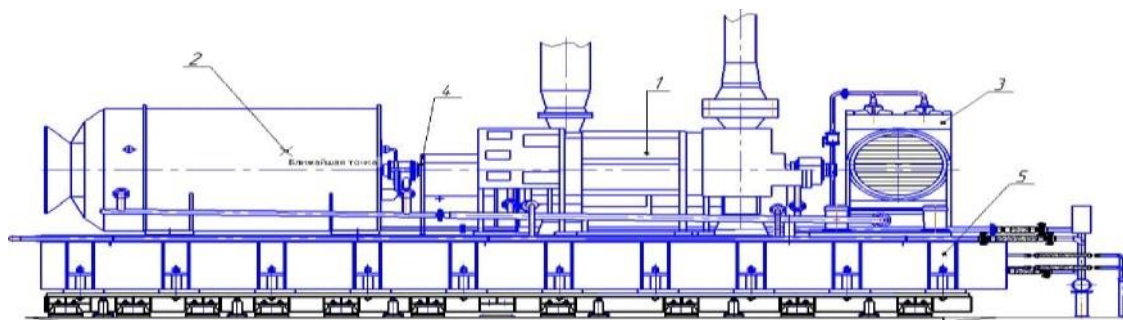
Насосний агрегат ЦНС 500 — 1900
